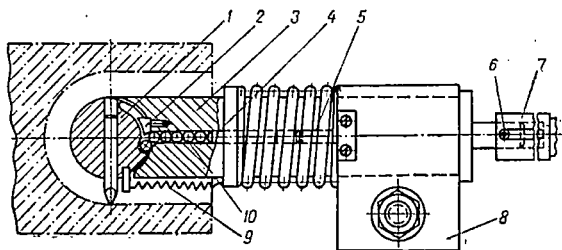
Приспособление для чистовой расточки сферических поверхностей в глубине детали.
